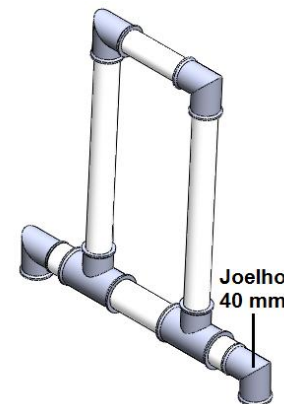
Montagem dos módulos – Módulo 4 – Passo 7
